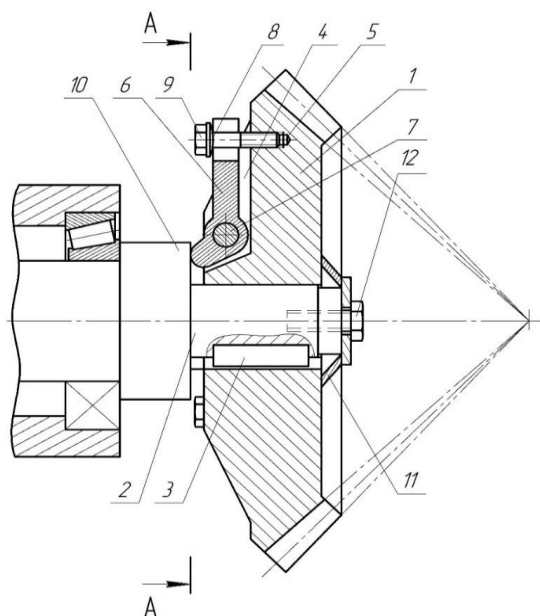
Пристрій для регулювання зачеплення конічних шестерень
